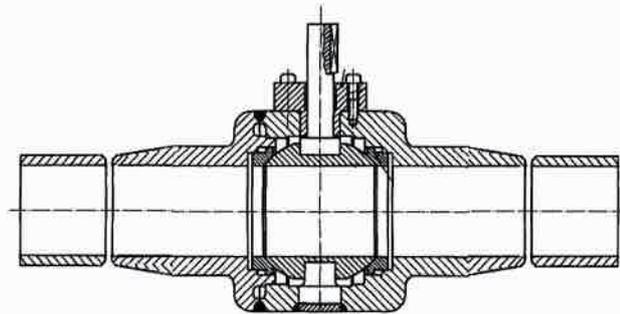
Esquema de instalación para soldadura, todas las válvulas vienen preparadas para soldar
